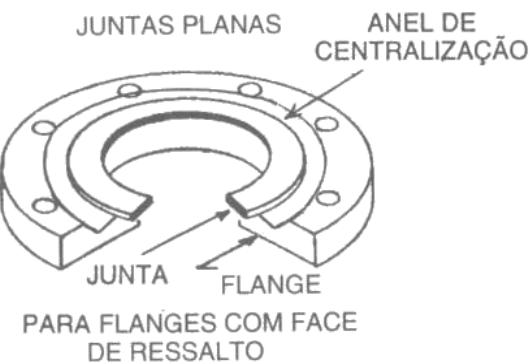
Junta de compressão plana, em forma de coroa circular, para flanges com face de ressalto.
